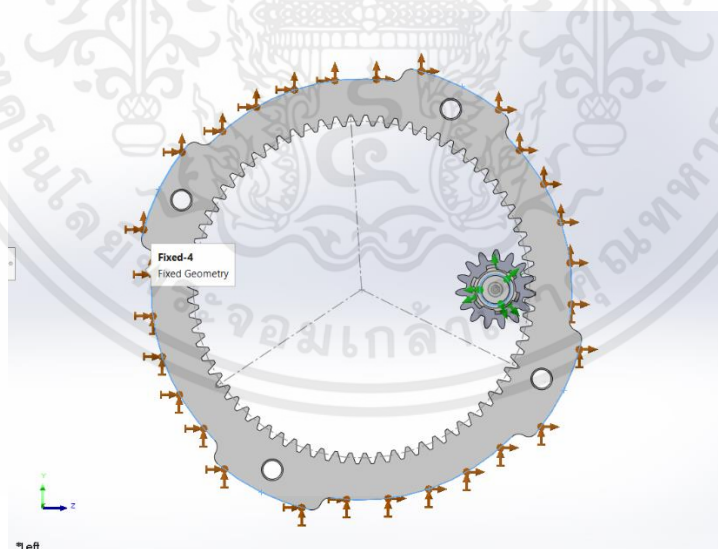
แสดงชิ้นงานส่วน Ring gear กับ planet gear
